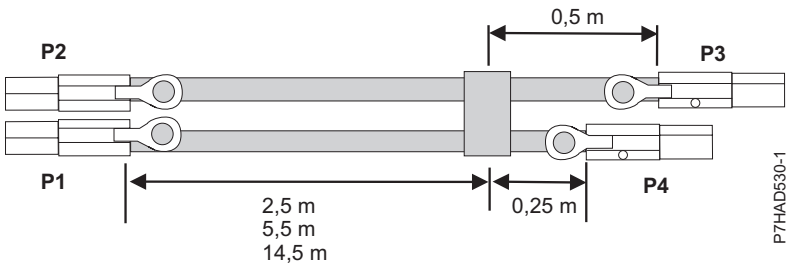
Longituds de cables de conjunt de cable X SAS extern
